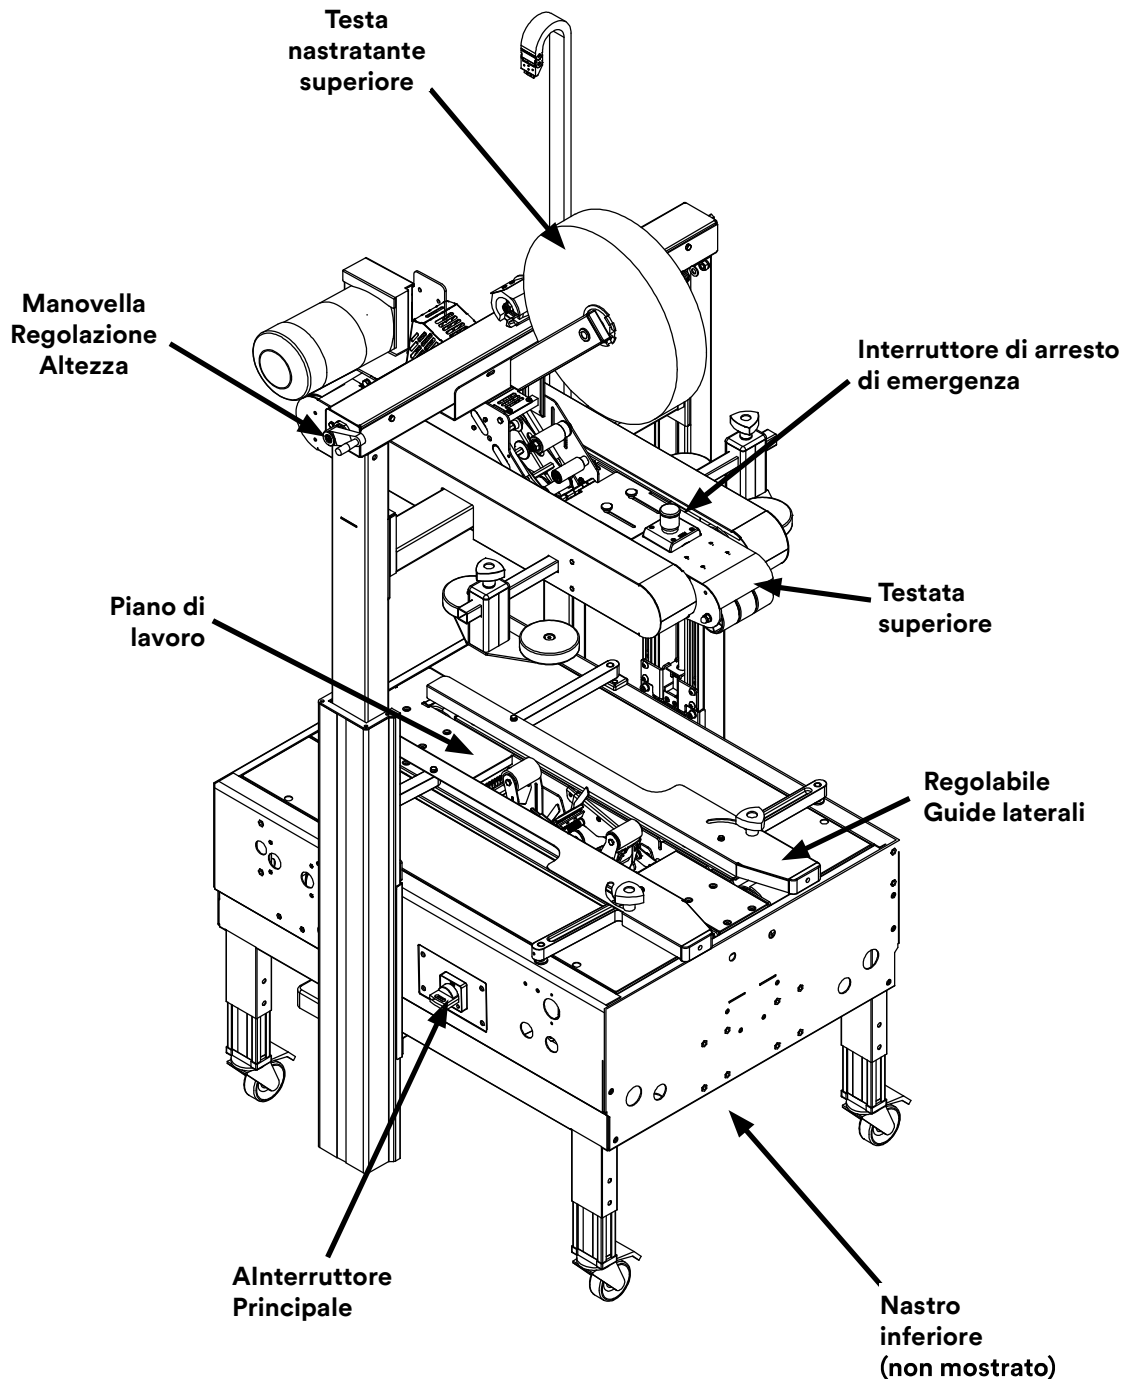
7000a-I / 7000a3-I Componenti del sistema di sigillatura (Vista frontale sinistra)
